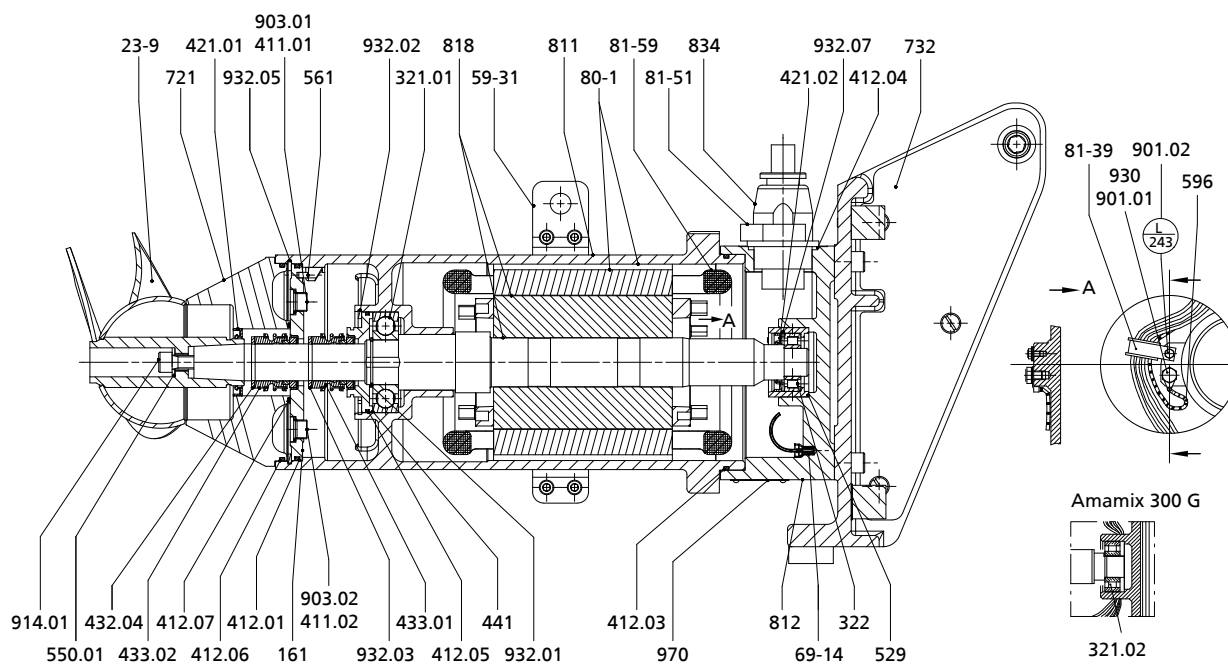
Чертеж общего вида Amamix 300/400/600, материал корпуса двигателя – серый чугун
